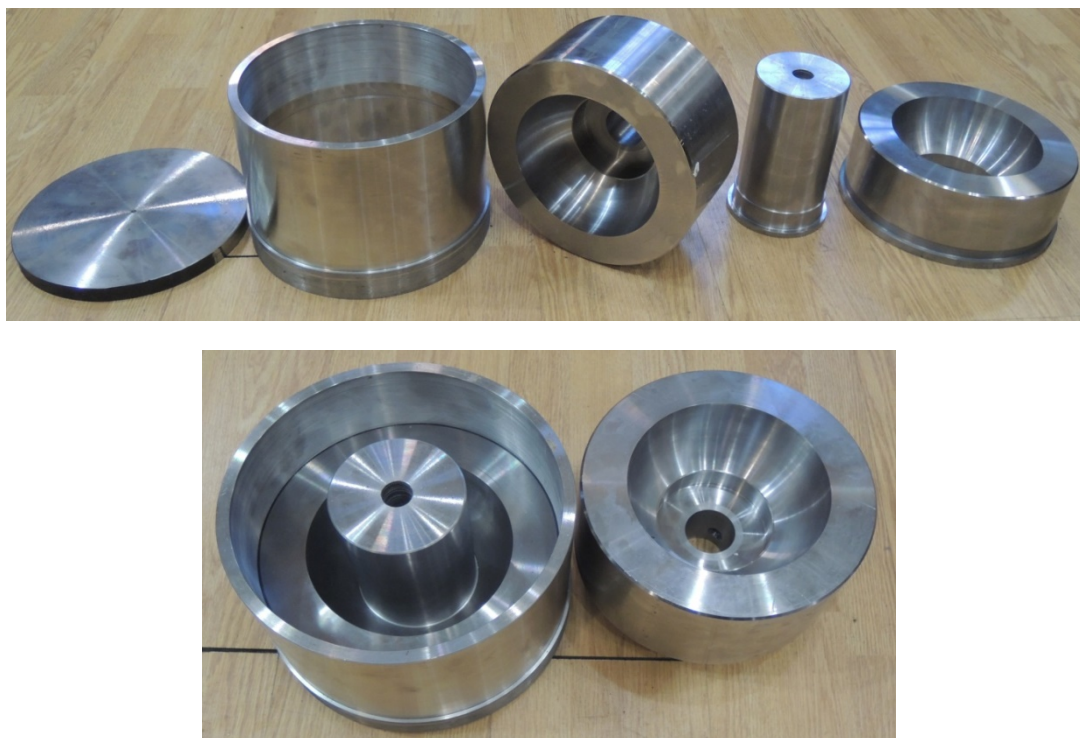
Детали штампа для обжима сферической пробки DN100
